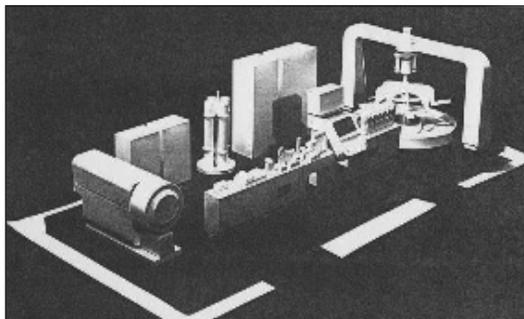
Макет промышленного образца стана АДСТ с порталом для сброса полученной трубной заготовки в корзину волочильного барабанного стана
